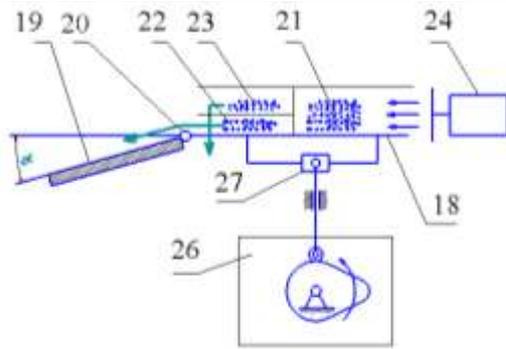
Схема привода части совершающей колебательное движение сортировочного механизма
